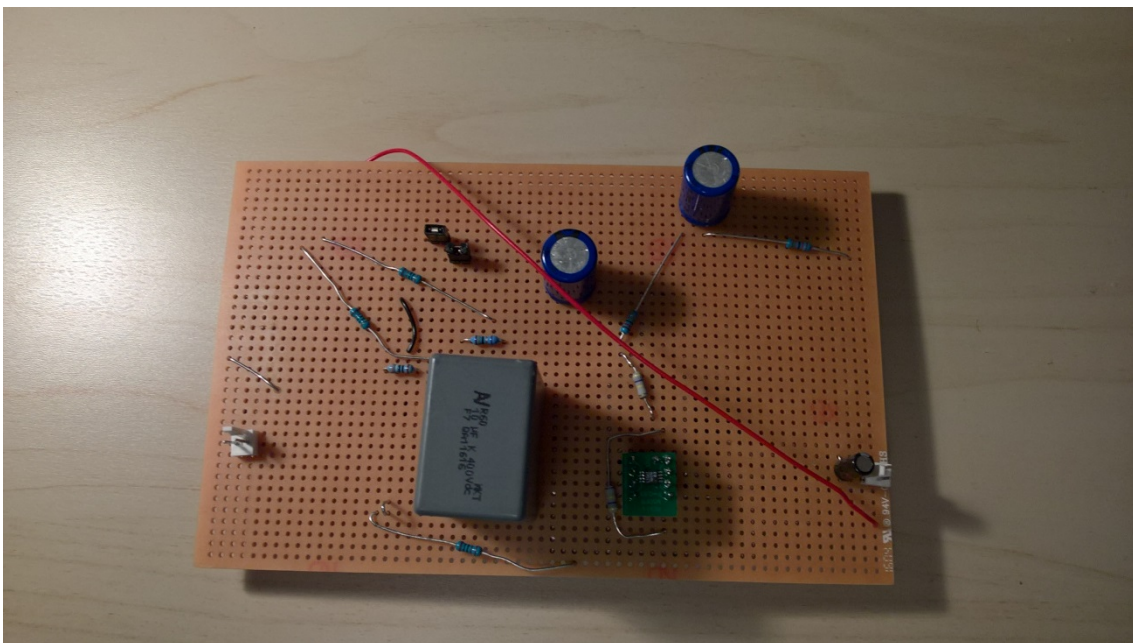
Vista de la parte no soldable de la placa de prototipado.
